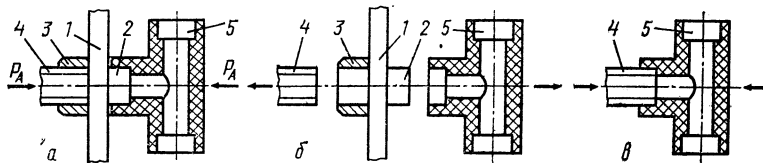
Принцип сварки раструб фитингов и втулок: а — подогрев свариваемых деталей; б — отвод нагретого инструмента; в — состыковка (сварка); 1 — нагретый инструмент; 2 — нагретый (сварочный) дорн; 3 — нагретая (сварочная) гильза; 4 — пластмассовая труба; 5 — пластмассовый фитинг
